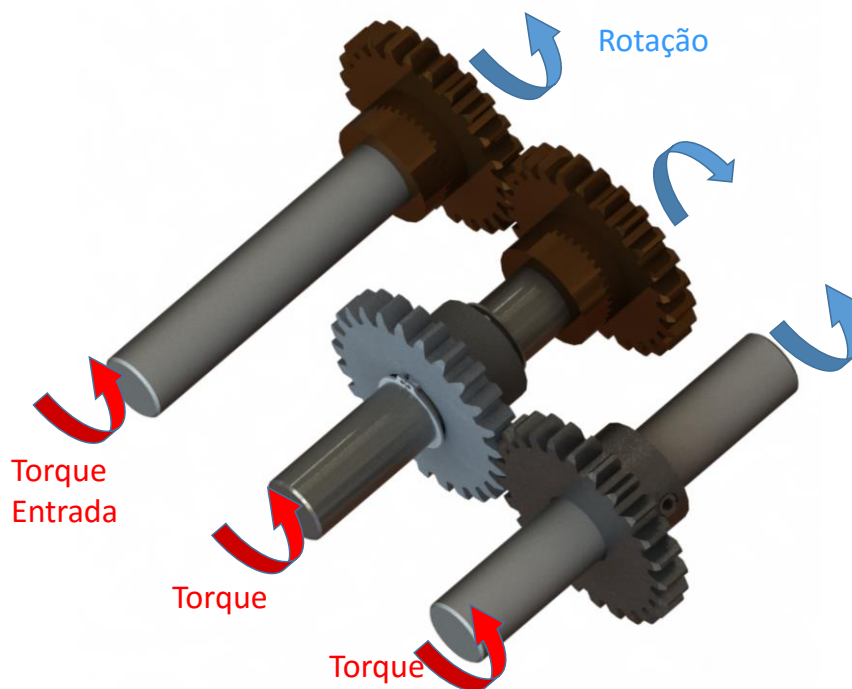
Eixos paralelos transmitindo torque a partir de engrenagens cilíndricas de dentes retos
